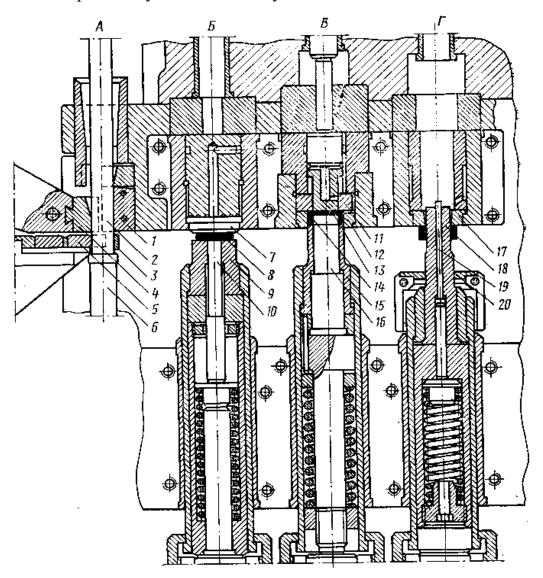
Схема штамповочного инструмента многопозиционного горячештамповочного автомата АМР-30 для изготовления поковок подшипниковых колец:
